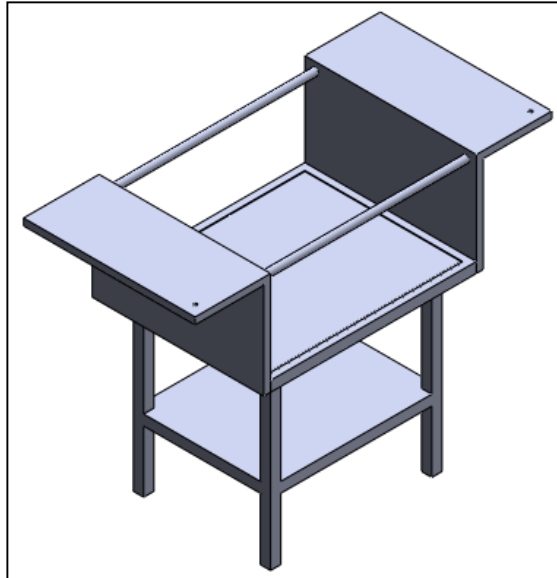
Vista isométrica del ensamblaje 2 de la máquina cortadora de vidrio
